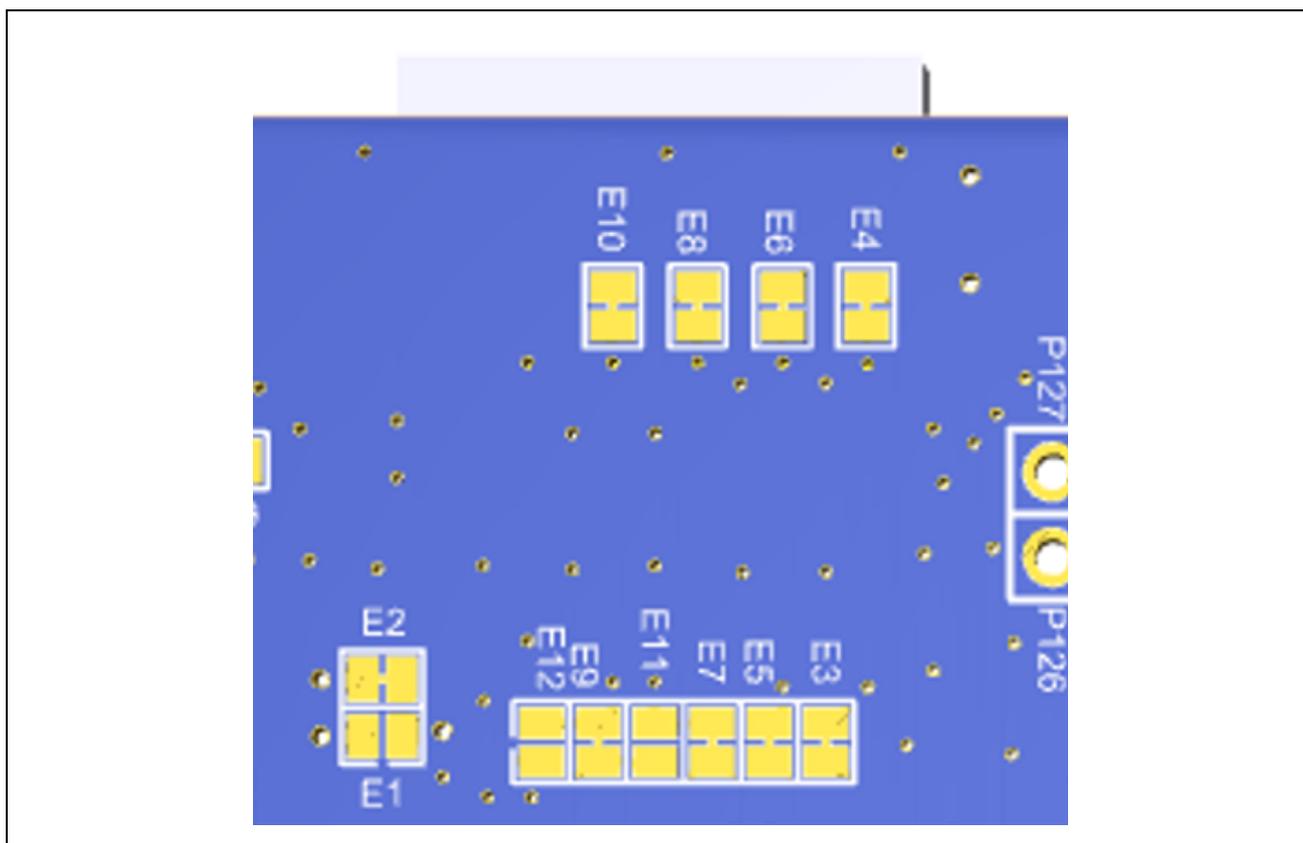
Pmod 1 Jumper Trace Cut / Solder Bridge 配置 (はんだ面)
